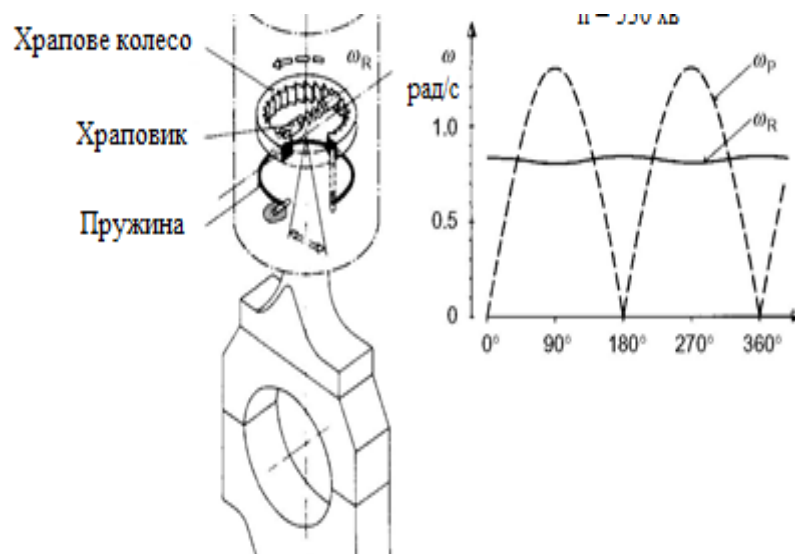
Принцип роботи обертового поршня: ω_p – кутова швидкість обертання поршня;
